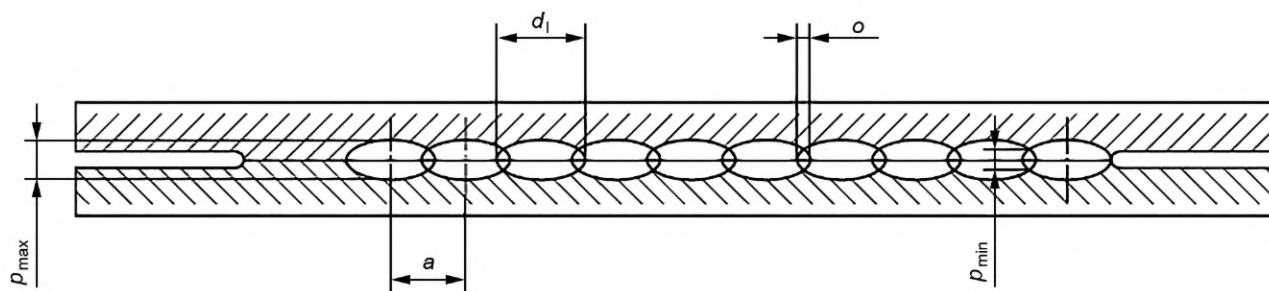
Типовые схемы контактной двусторонней сварки
